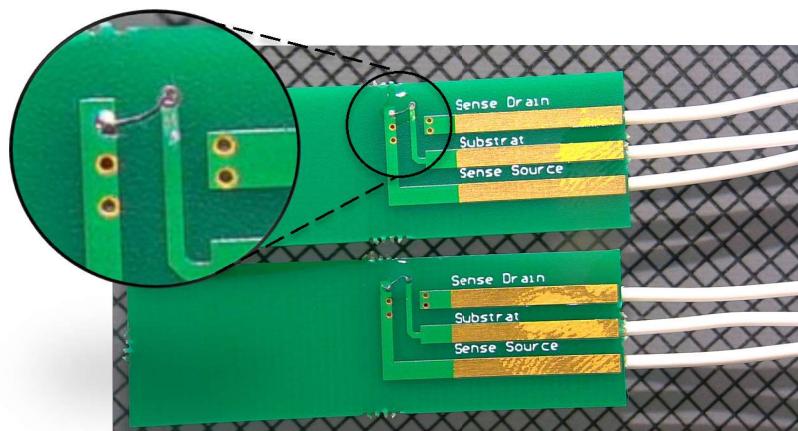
Carte PCB avec la puce RÉFÉRENCE_1 (côté bonding)
